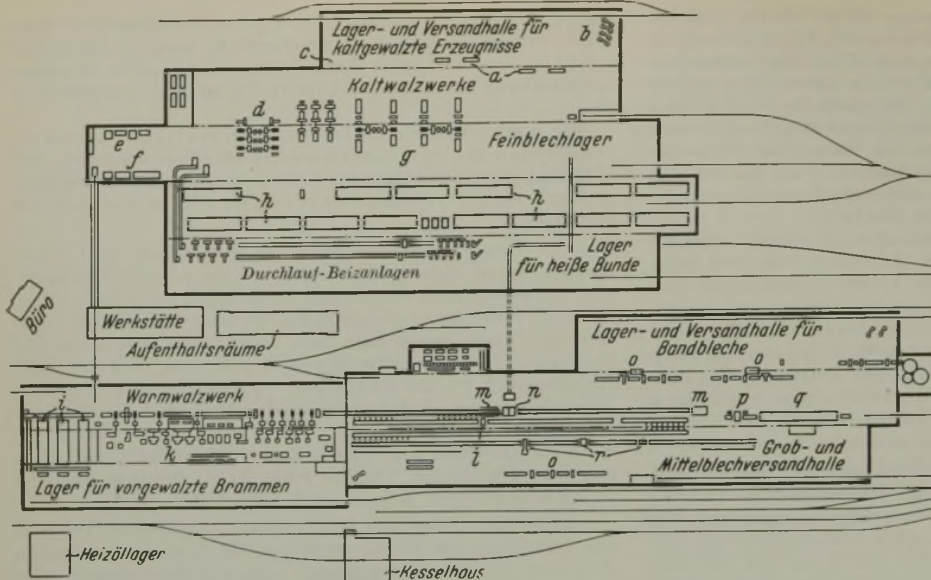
Grundriß der Warm- und Kaltwalzwerksanlagen.
